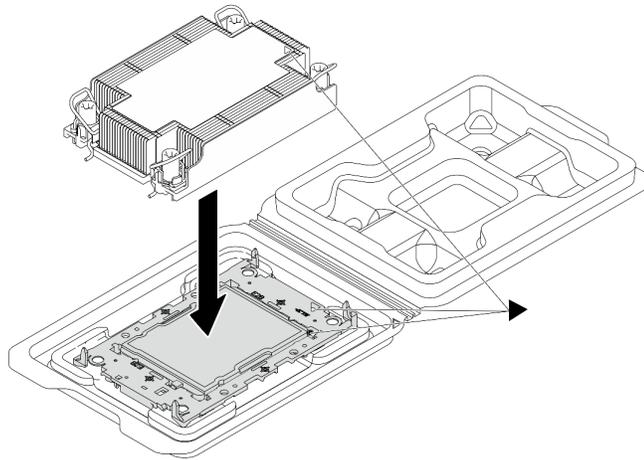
Assemblage du module de processeur-dissipateur thermique avec le processeur dans le plateau d'expédition
